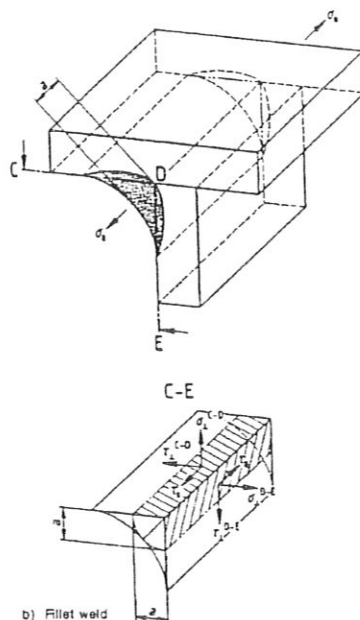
assemblage soudée (selon DIN 18 800-1)
